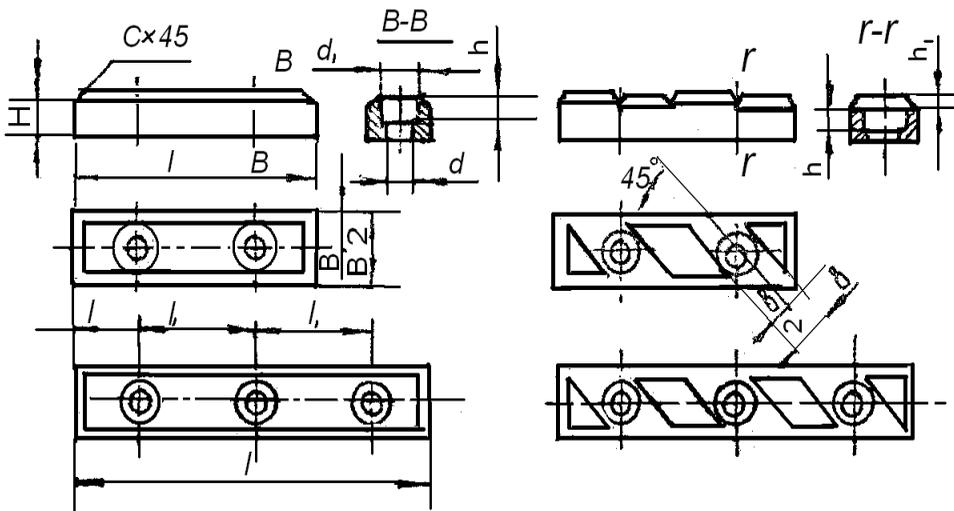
Пластины опорные: а) плоские; б) с косыми пазами.
